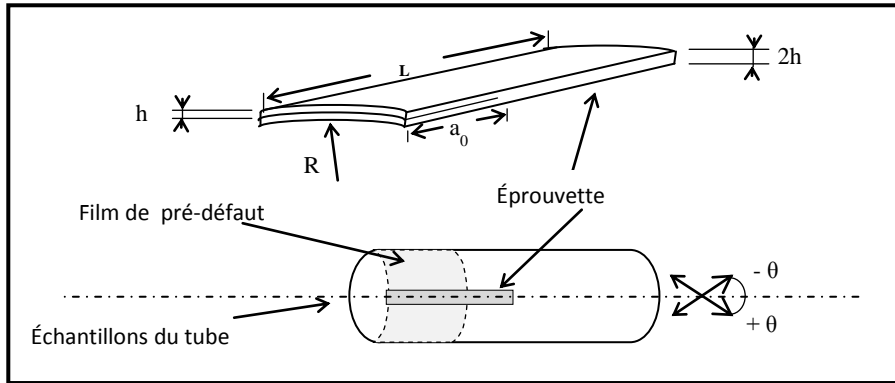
Schéma de la première méthode de découpage des éprouvettes DCB.
